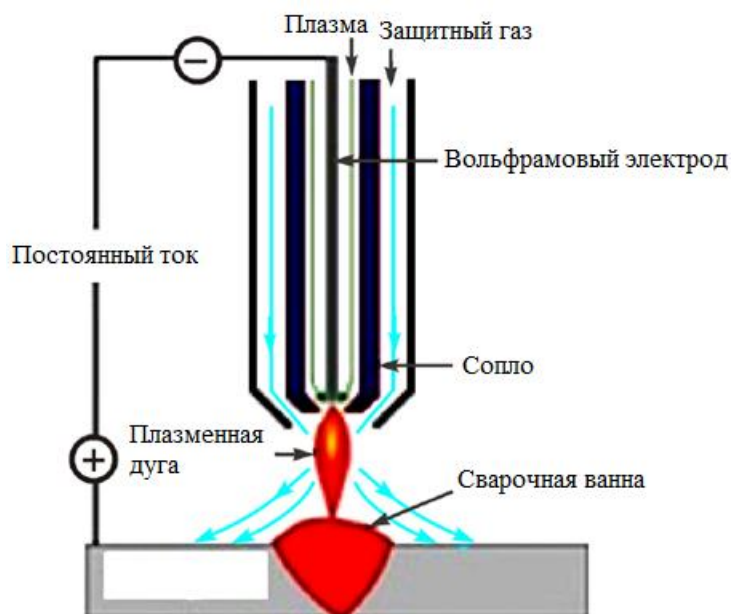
Схема процесса плазменной дуговой сварки [11]
